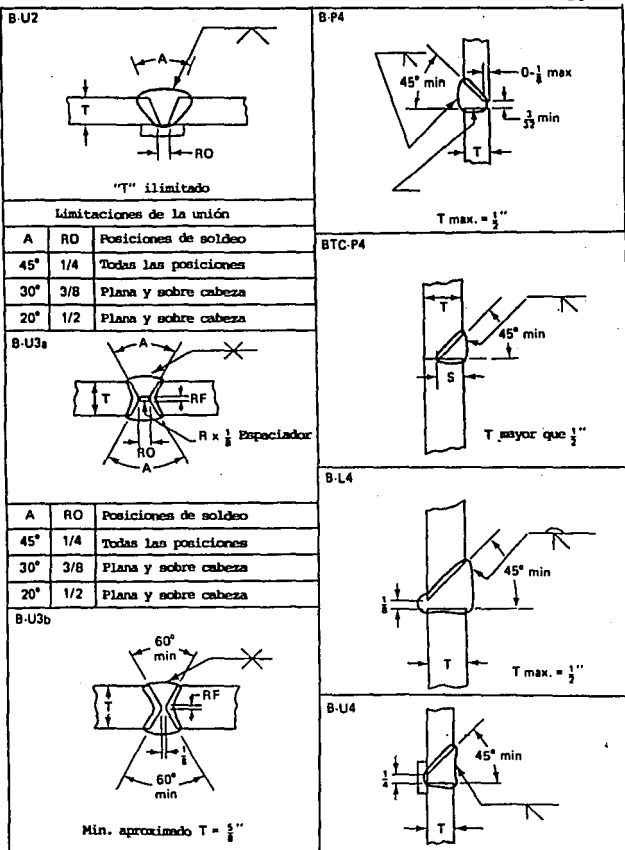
Diseño de uniones soldadas (cont.).
